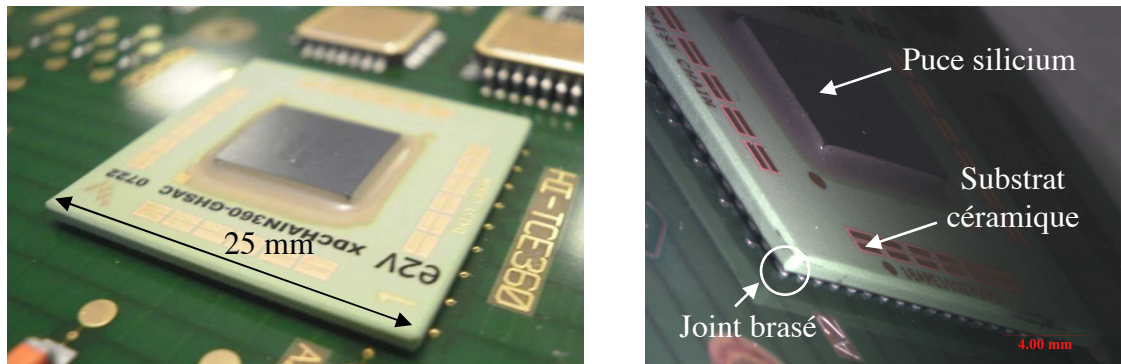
Vues d'ensemble du composant de type HITCE360 assemblé
